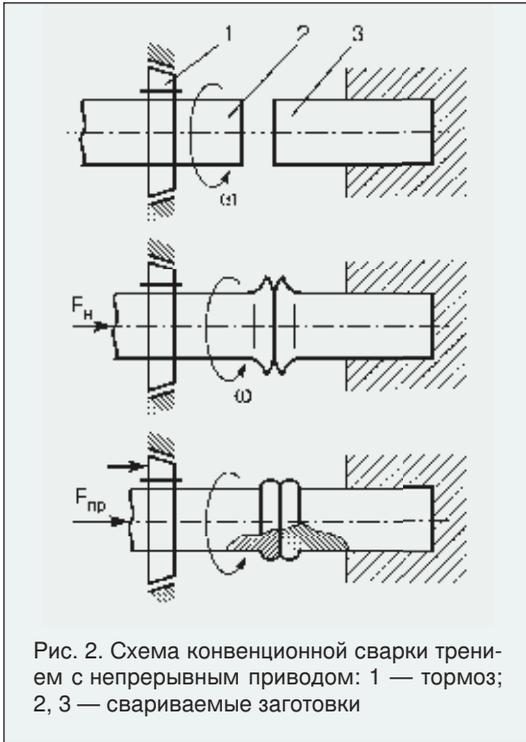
Схема конвенциональной сварки трением с непрерывным приводом: 1 — тормоз; 2, 3 — свариваемые заготовки
